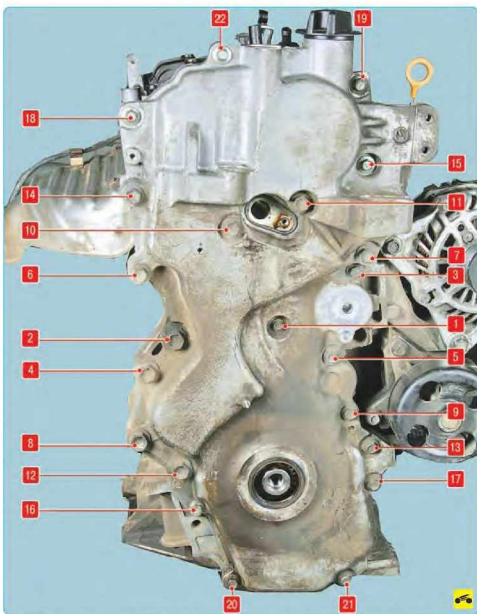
Последовательность затяжки болтов крепления крышки газораспределительного механизма
